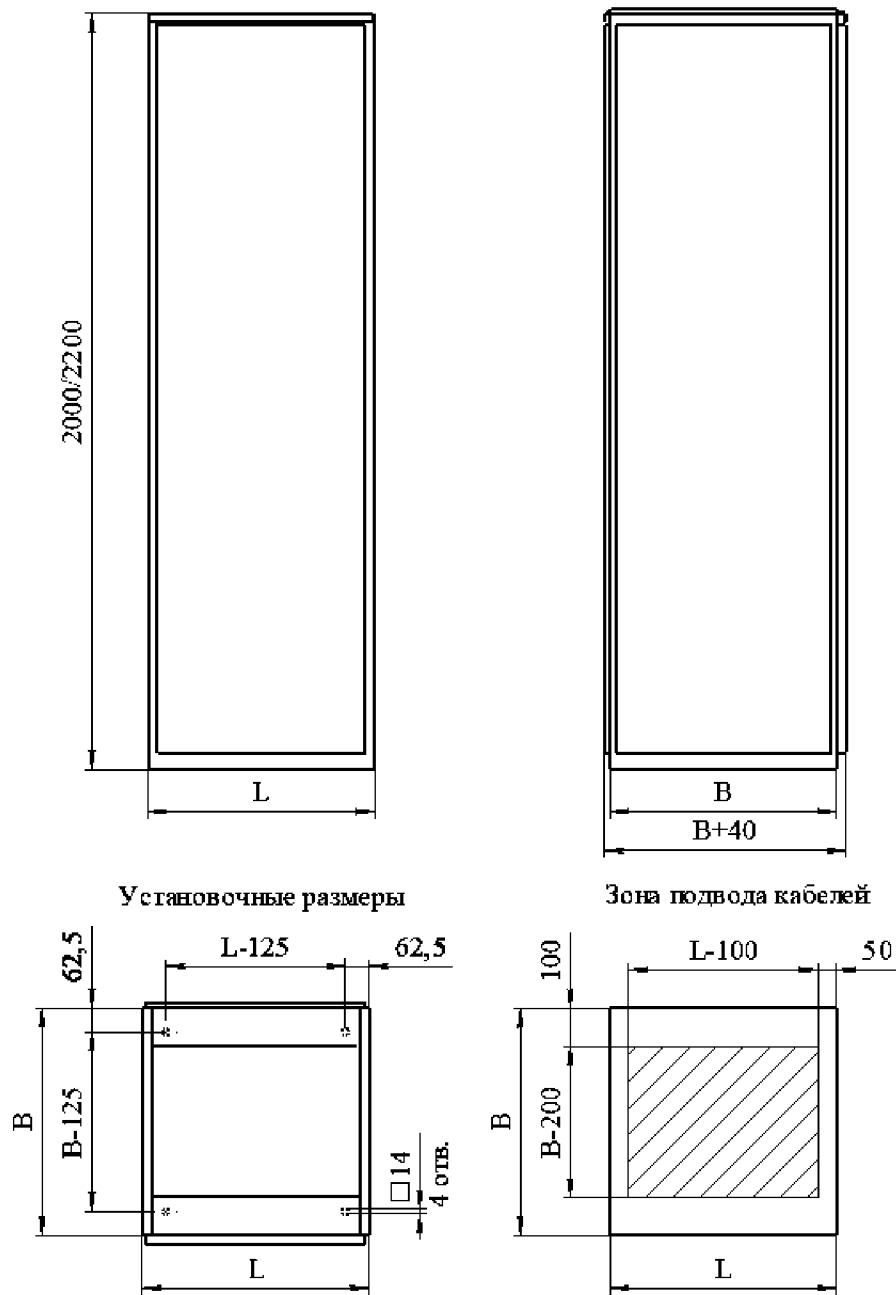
Исполнения металлоконструкции шкафов
